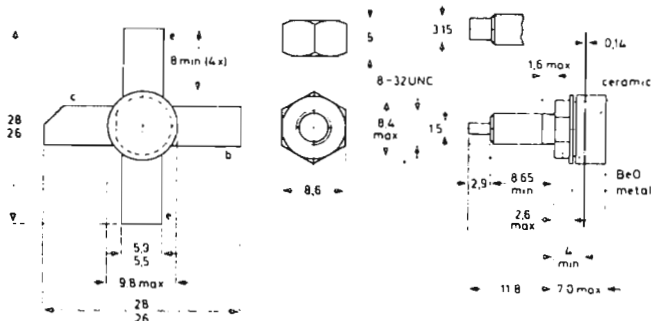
Dimensioni di ingombro in mm del transistor BLW 29.
